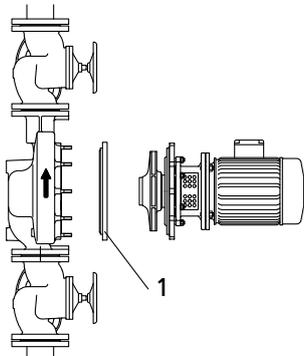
Horizontaler Einbau mit Blindflansch (1 = Blindflansch, Zubehör)
